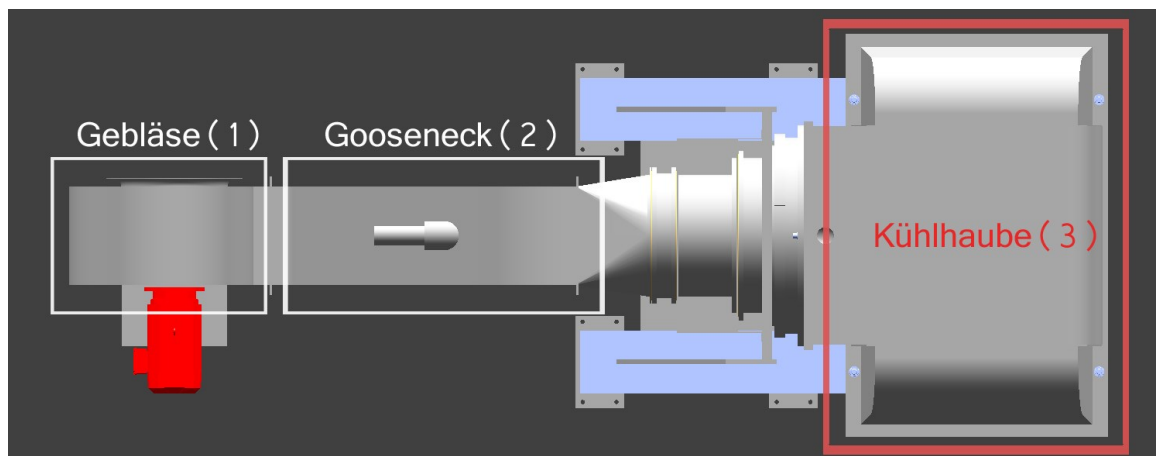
Prototyp des Schlackenkühlers - Grundriss
